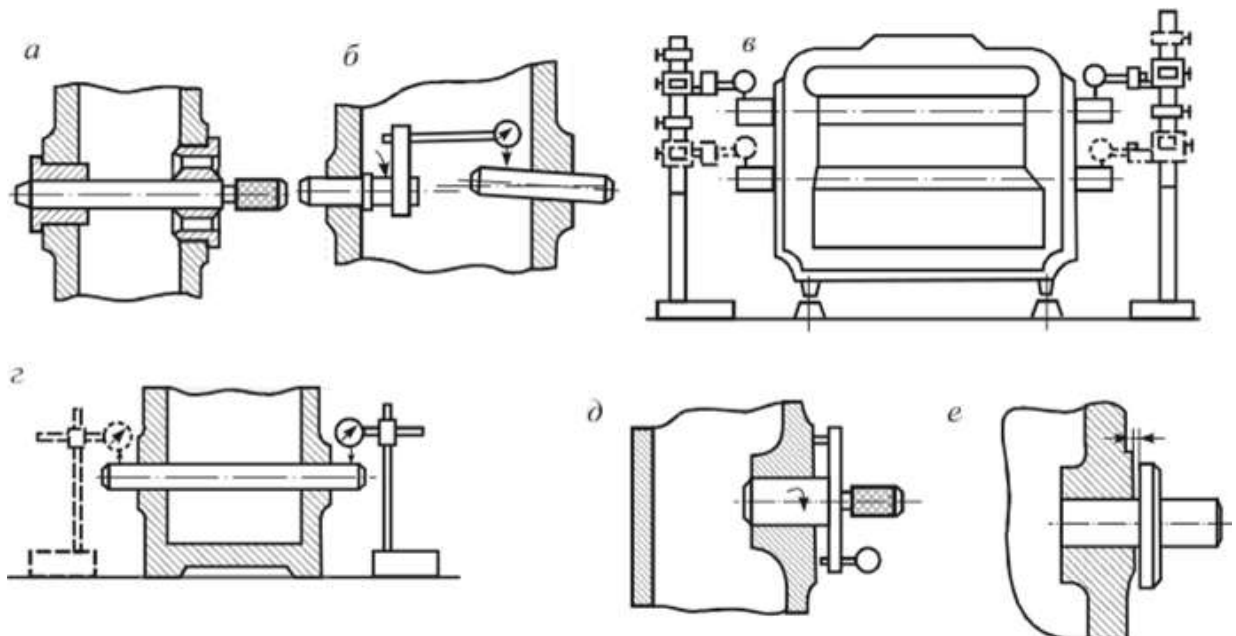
Схеми контролю розташування поверхонь корпусної деталі
